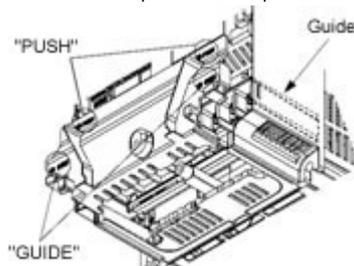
Montage du couvercle du bornier du circuit principal
